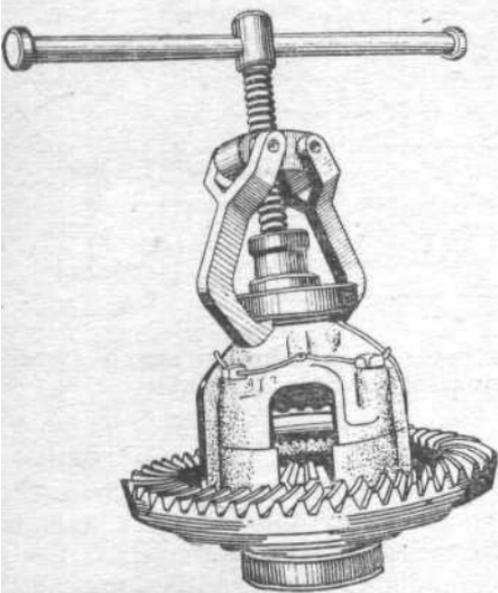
Съемник внутреннего кольца подшипника коробки дифференциала
